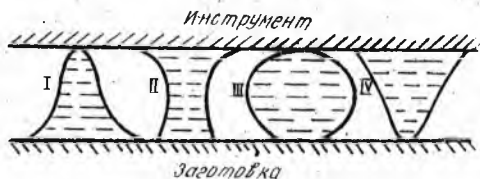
Формы капель смазки, наносимой на инструмент или заготовку
